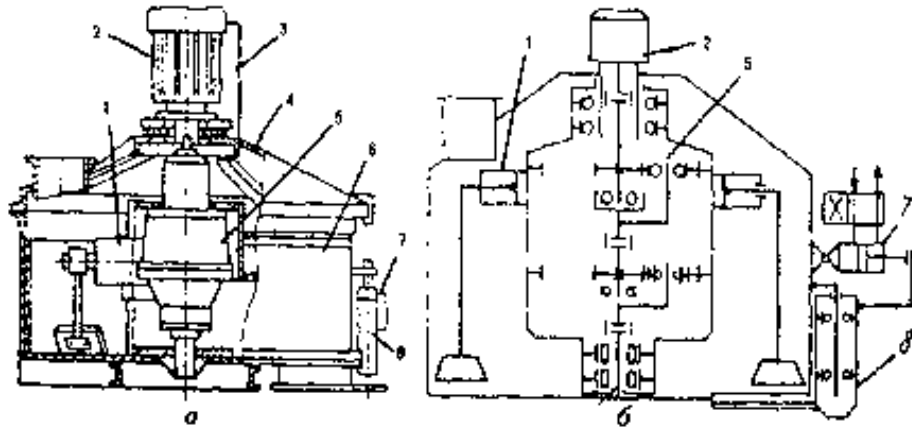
Роторний змішувач з планетарним редуктором
